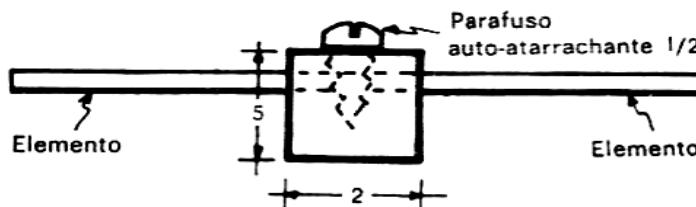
Com o emprego de um parafuso auto-atarrachante, evitaremos que os elementos deslizem transversalmente à gôndola.
